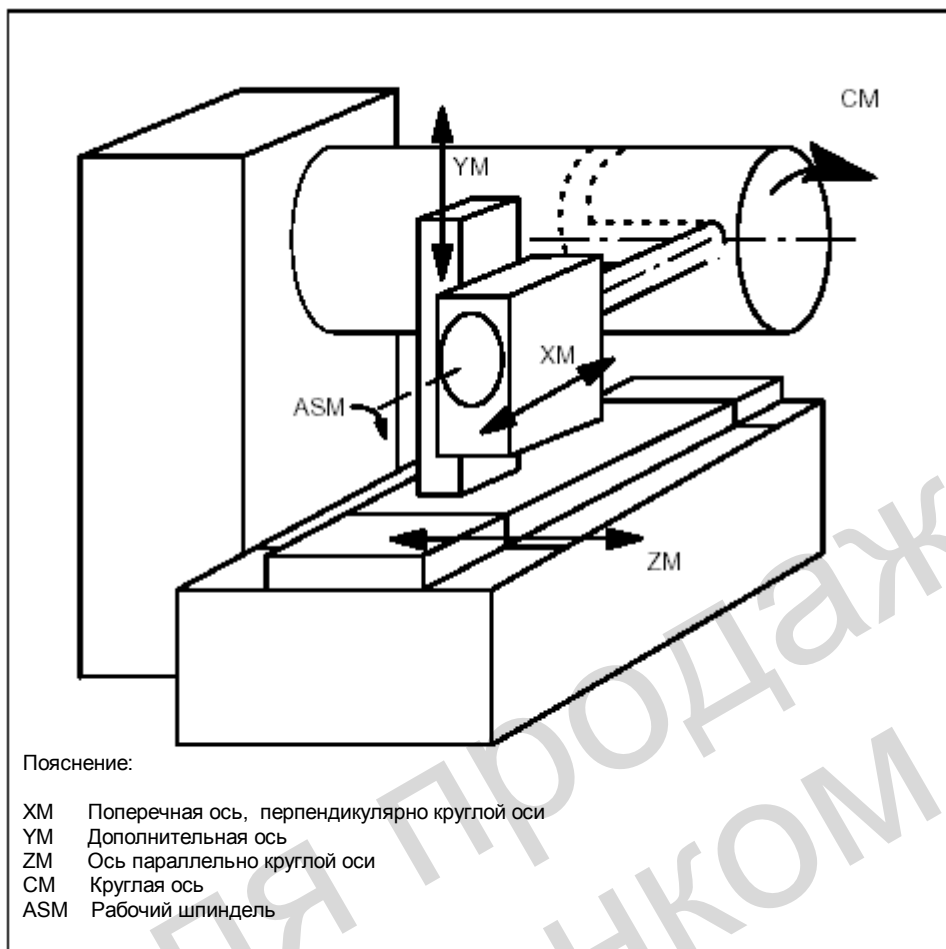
Обработка паза на боковой поверхности цилиндра с помощью кинематики X-Y-Z-C.
